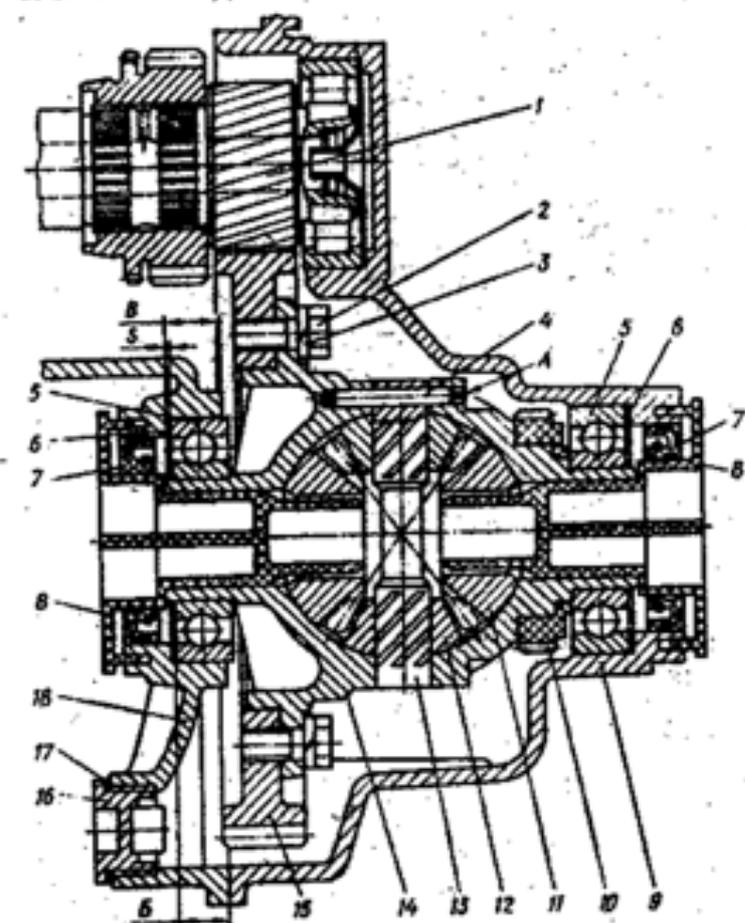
Главная передача с дифференциалом: 1 - шестерня ведущая главной передачи; 2 - болт; 3 - шайба пружинная; 4 - штифт; 5 - подшипник дифференциала шариковый; 6 - прокладка регулировочная; 7 - манжета; 8 - крышка транспортного; 9 - картер сцепления; 10 - шестерня ведущая привода спидометра; 11 - шестерня полуоси; 12 - сателлит дифференциала; 13 - ось сателлитов дифференциала; 14 - коробка дифференциала; 15 - шестерня главной передачи; 16 - пробка сливная; 17 - прокладка; 18 - картер коробки передач; А - после запрессовки штифта кернить
